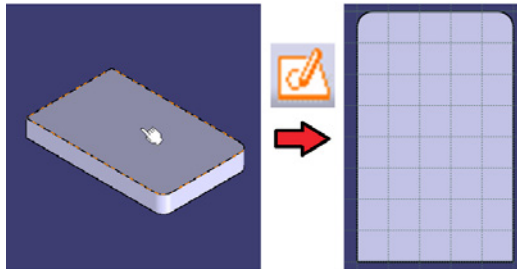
Bauteiloberfläche als Stützelement für eine neue Sketch
